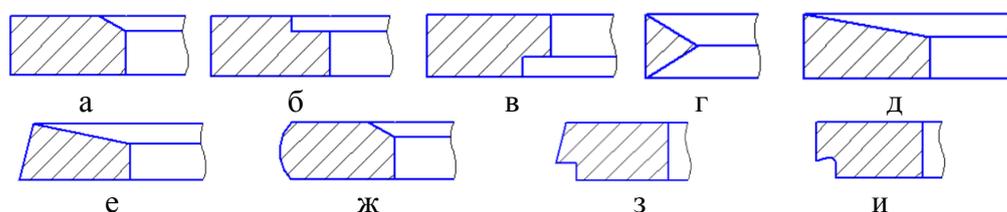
Профили поршневых колец: а – прямоугольный; б – с верхним внутренним углом; в – с нижним внутренним углом; г – трапециевидный; д – несимметричный трапециевидный; е – конический; ж – бочкообразный; з – конический скребковый; и – скребковый
